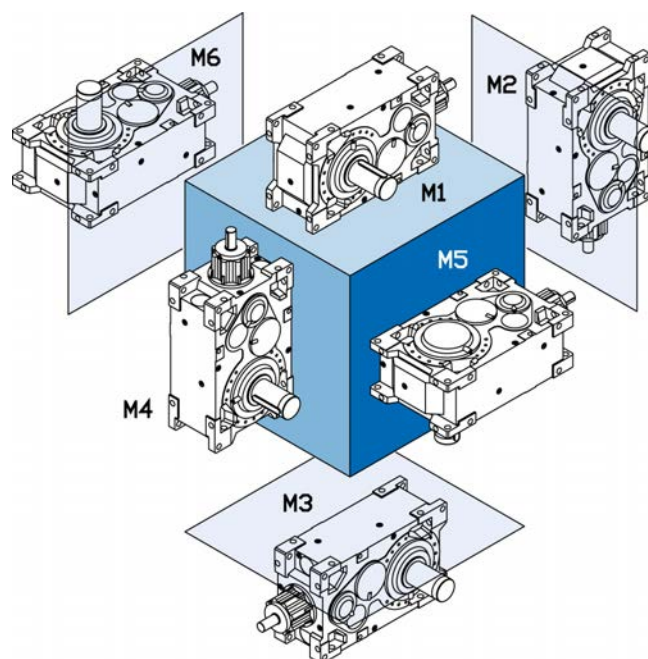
Positions de montage du réducteur à couple conique avec surface de montage standard
